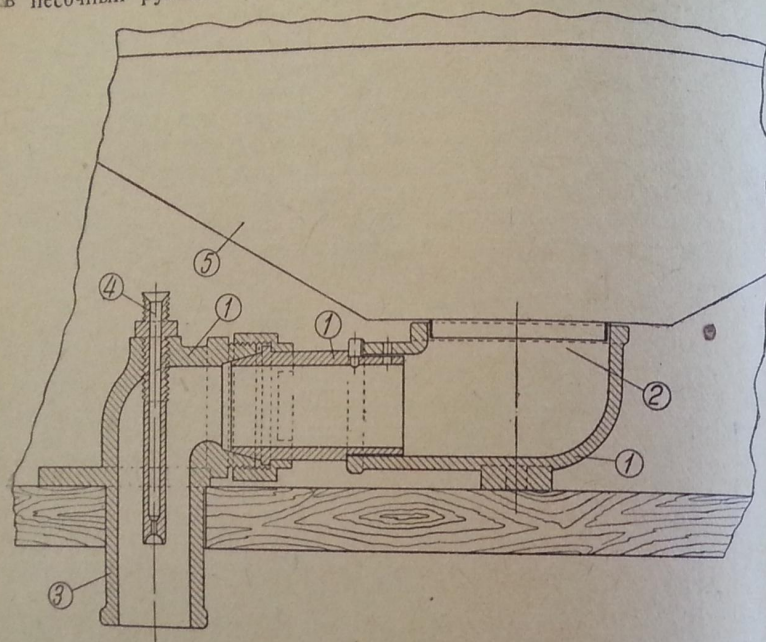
Воздушная песочница Плащинского: 1 — корпус, 2 — отверстие, 3 — патрубок, 4 — сопло, 5 — песочный ящик.
